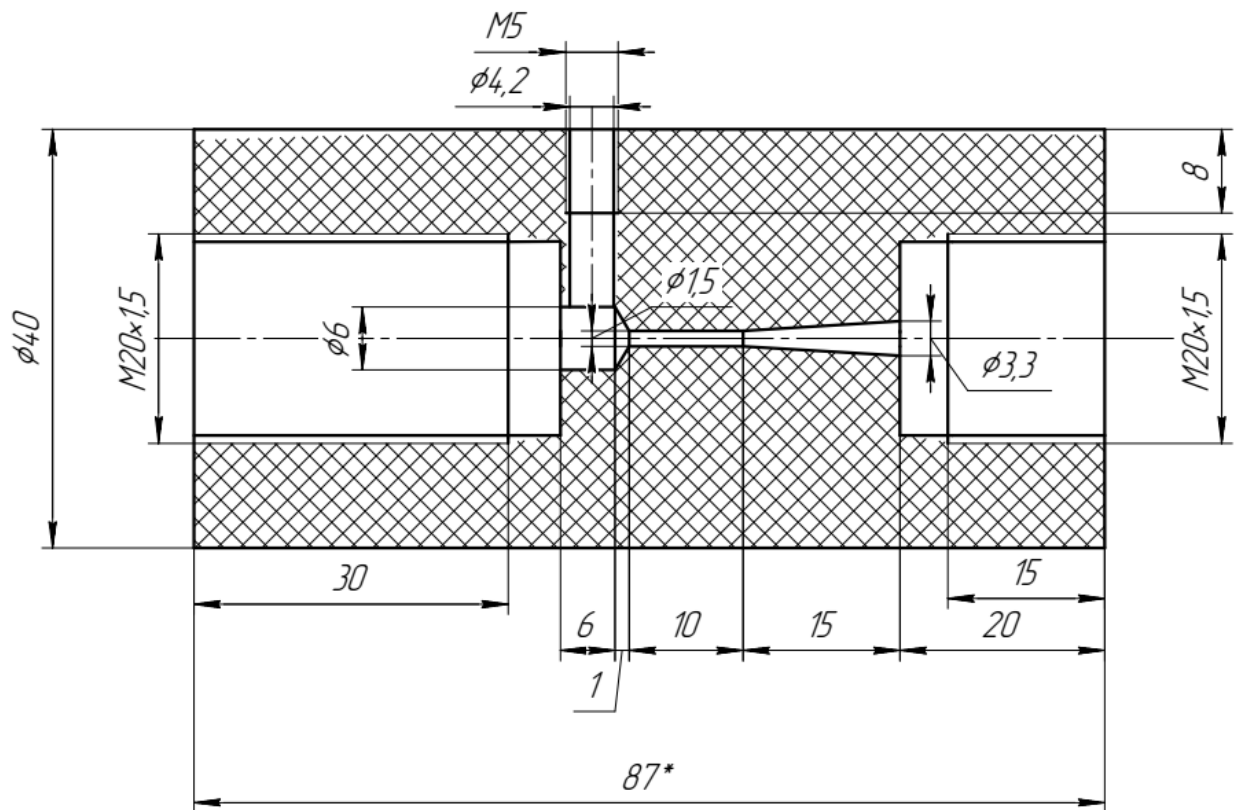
Креслення деталі «Корпус ежектора»
